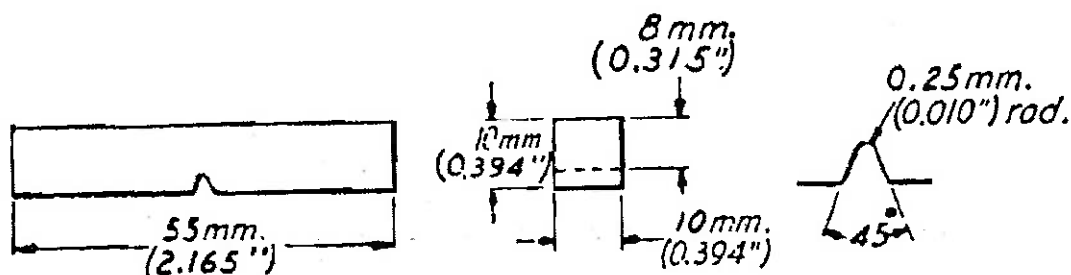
Dimensões do corpo de prova de impacto Charpy com entalhe em V.
